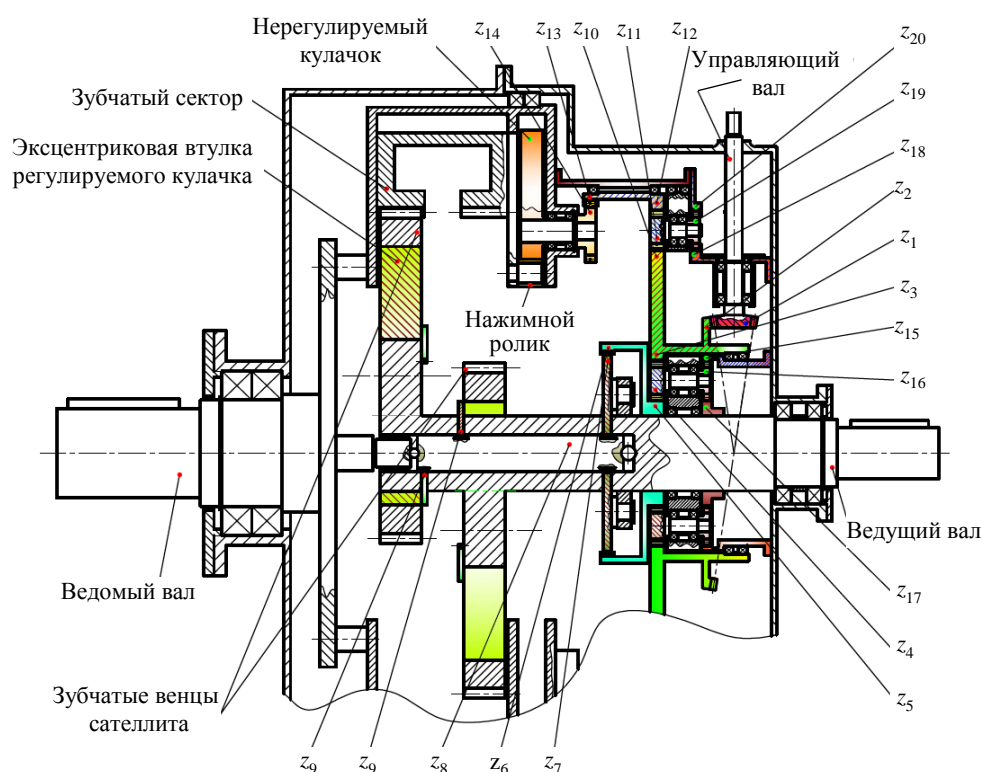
Схема кинематической цепи управления передаточным отношением ППП при oppositно расположении зубчатых венцов сателлита
